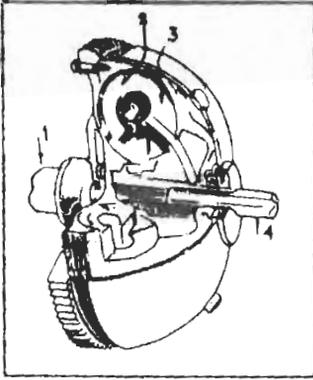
Embrague hidráulico. 1.- Cigüeñal. 2.- Impulsor o bomba. 3.- Turbina. 4.- Eje de transmisión.
